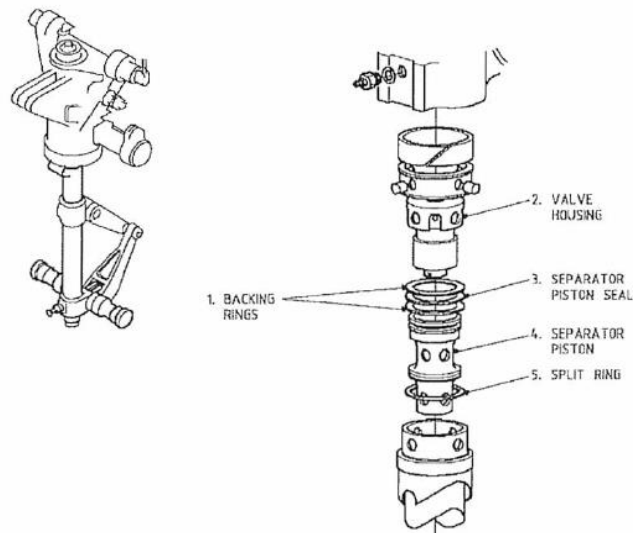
highlighting, in TASK 32-21-06-400-824-A, the valve housing.
